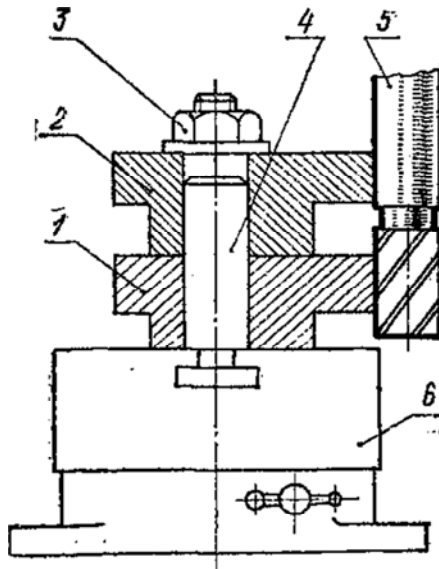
Фрезерование фасонной поверхности дискового кулачка по накладному копиру
